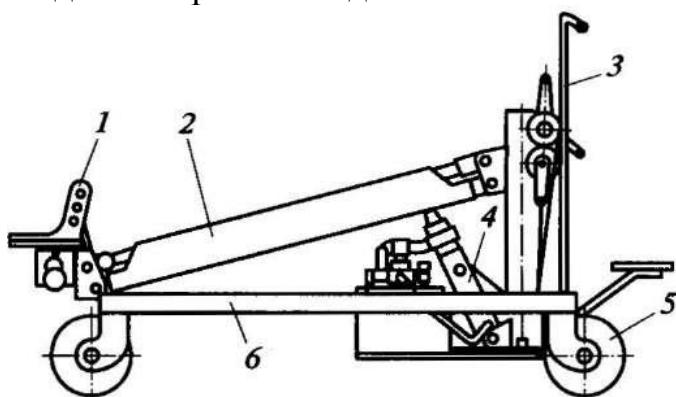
Тележка для снятия и постановки рессор: 1 — подхват для рессор; 2 — стрела; 3 — рукоятка; 4 — гидроцилиндр; 5 — колесо; 6 — щицольная балка
